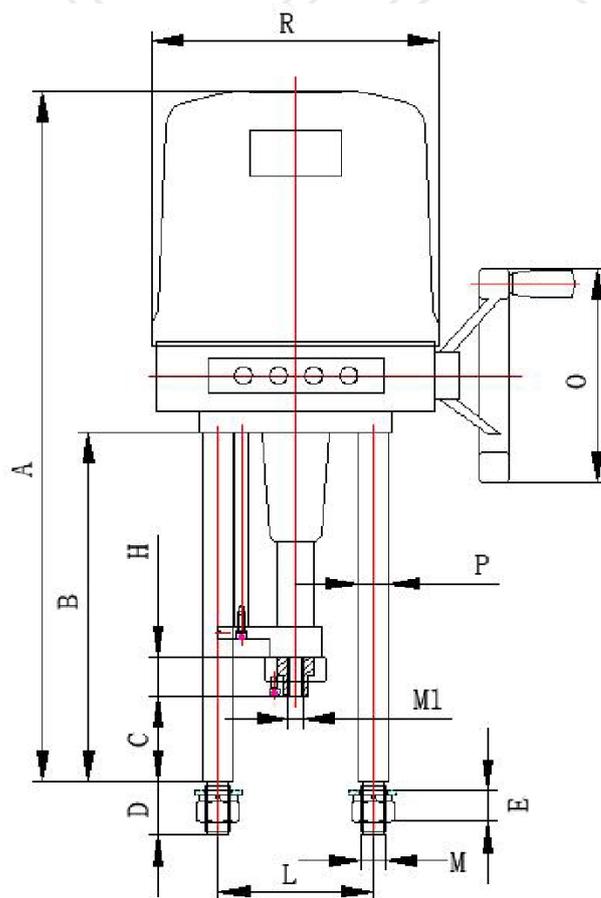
Внешний вид и габариты привода ПЭП-САЗ-1-(IN)
